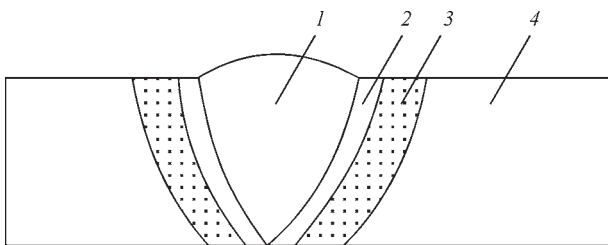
Схема будови структури металу зварних швів: 1 – зварний шов; 2 – зона сплавлення; 3 – зона термічного впливу (ЗТВ) зварювання; 4 – основний метал
